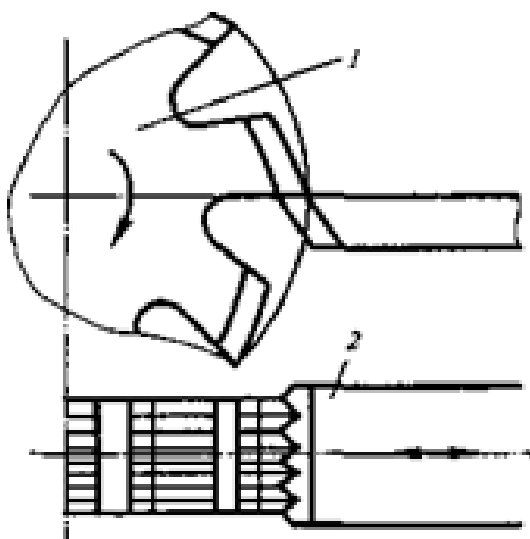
Схема радіального затилювання різьбової гребінчастої фрези: 1– різьбова фреза; 2 – гребінка
